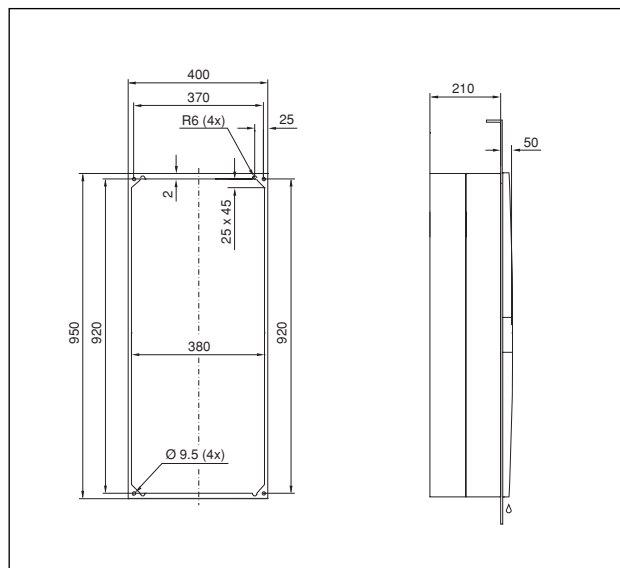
SK 3304.xxx, SK 3305.xxx til fuld indbygning
